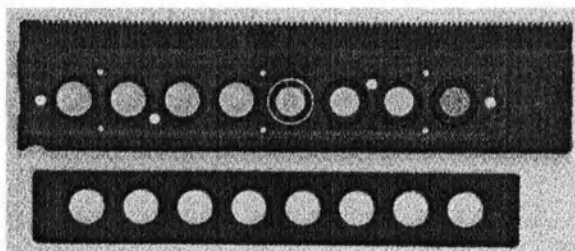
Держатель фильтров, готовый для установки фильтров
